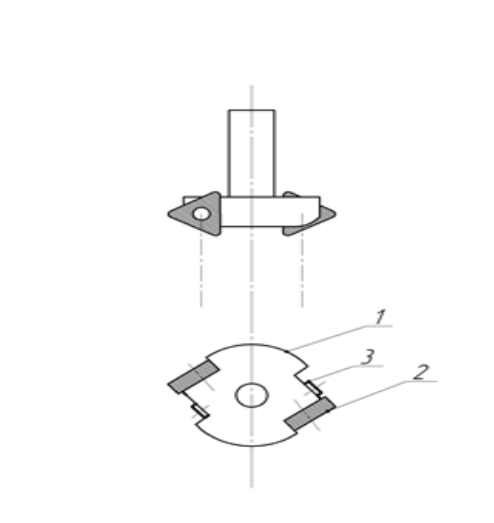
Сборный зенкер: 1-корпус зенкера, 2-режущая пластина, прижимной винт.
